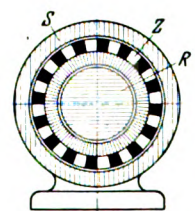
Doppelläufermotor mit 2 ineinandergeschachtelten asynchronen Systemen.
